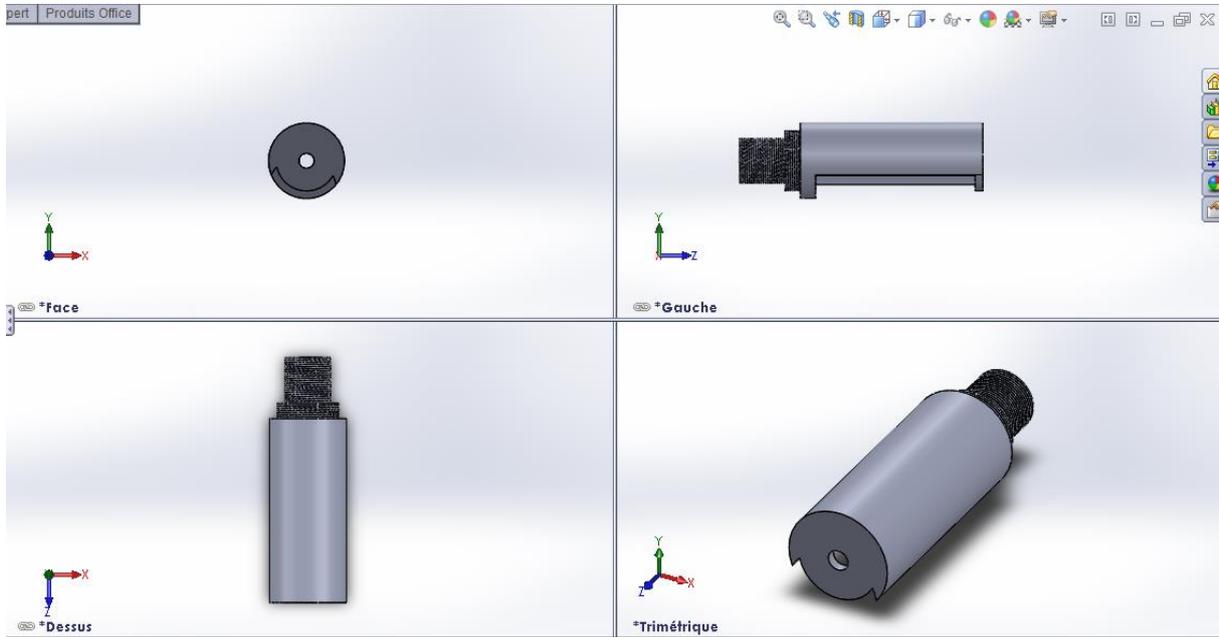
mise en plan solidworks du banc d'essai en dimensions réelles
